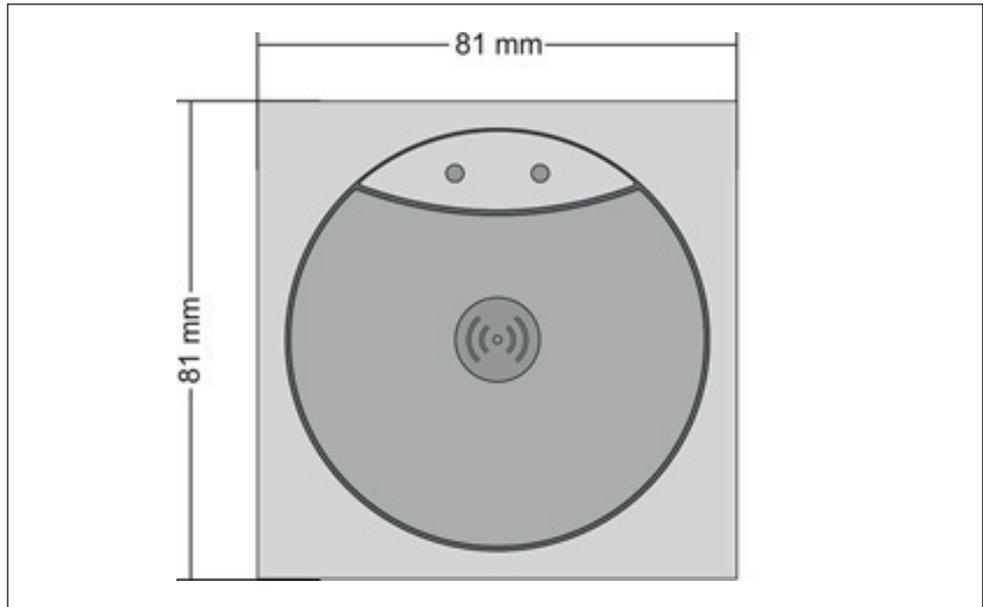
Ficha de dimensões do WT 210/WT 210 BLE com aro
